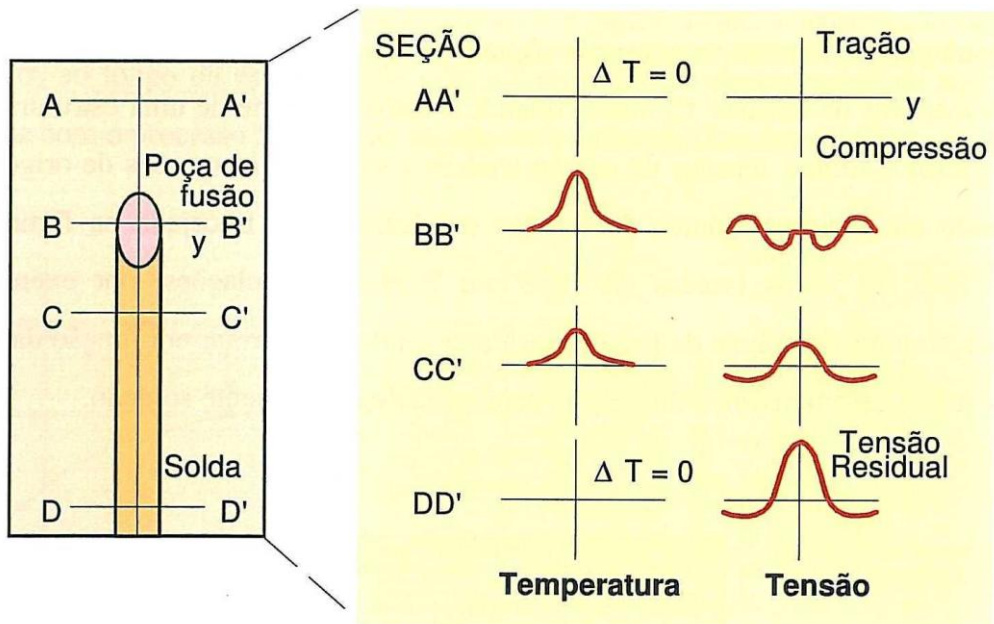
Desenvolvimento de tensões residuais longitudinais durante a soldadura
